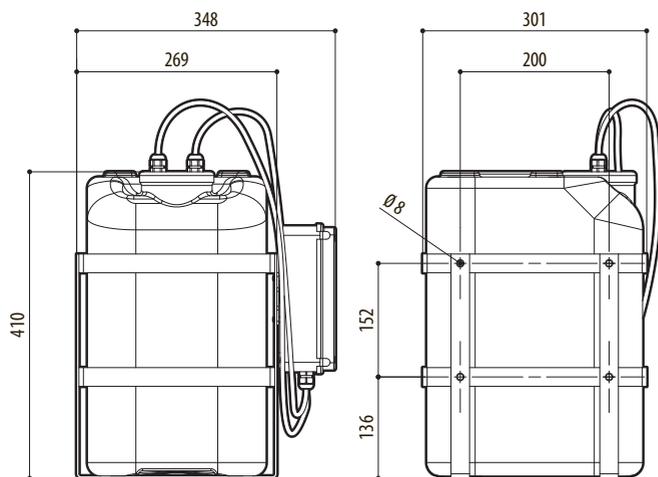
Réservoir 23l, hauteur de remontée de 5m ou 11m.
